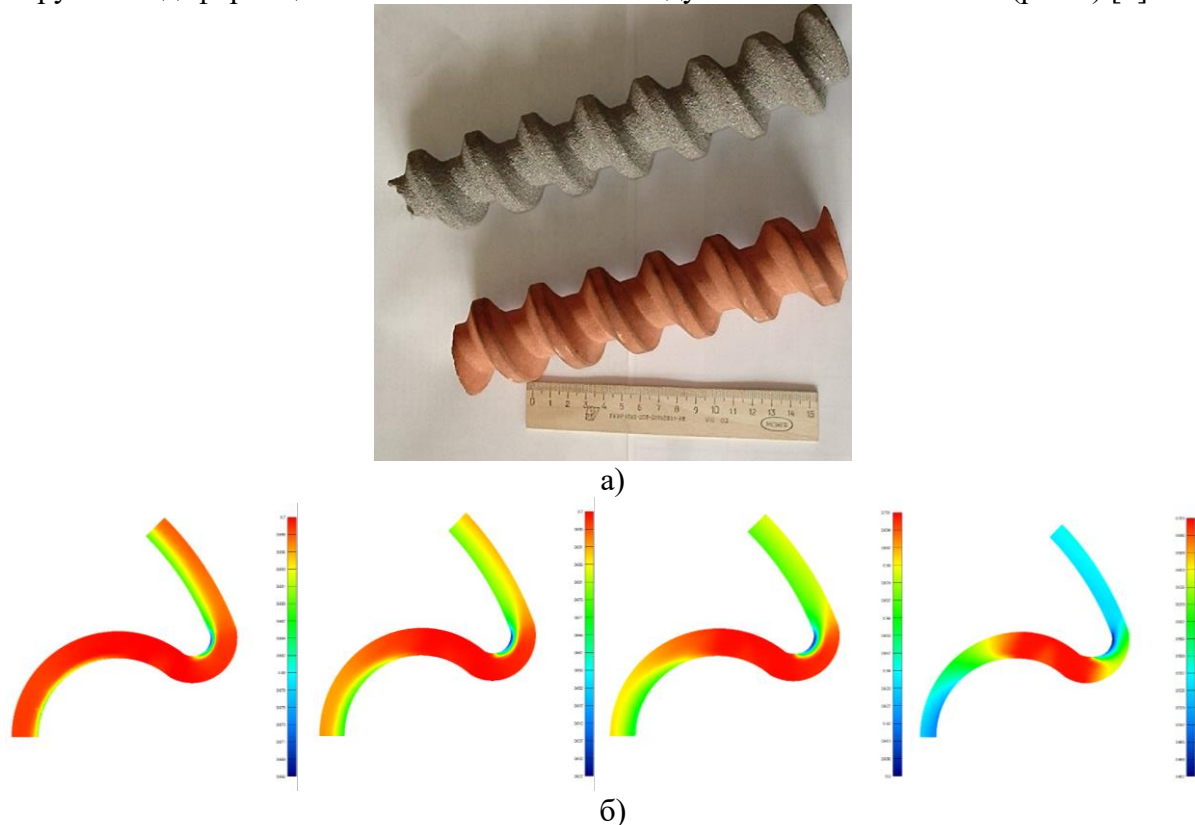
Загальний вид ППМ з розвинутою поверхнею (а) та визначення величин напружень по контуру пресовки ППМ (б)
